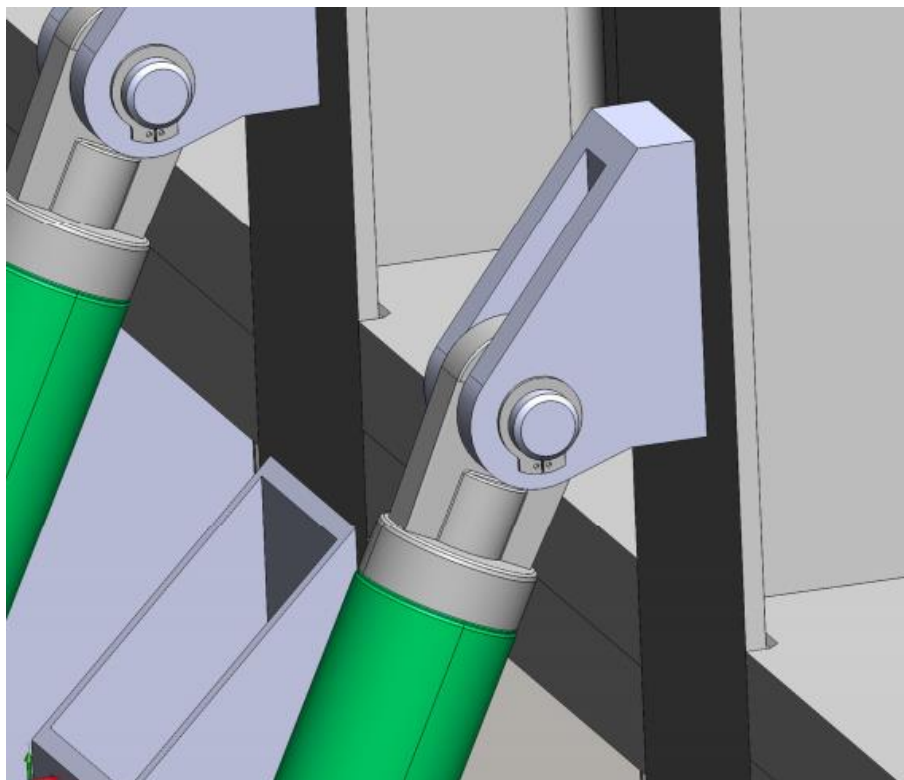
Ligação dos Cilindros hidráulicos à estrutura.
